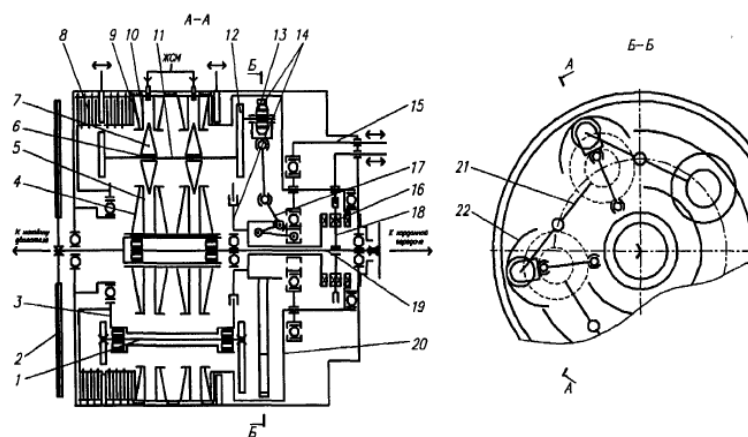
Схема автоматической бесступенчатой коробки передач автомобиля на основе нового планетарного дискового адаптивного вариатора: 1 — ось поворотных рычагов; 2 - соединительная муфта; 3 — водило; 4 — тарельчатая пружина; 5 — внутренний центральный фрикционный диск; 6 - подшипники сателлитов; 7 - сателлит; 8 — фрикционы; 9 — плоская дисковая пружина; 10 — внешний центральный фрикционный диск; 11 — ось сателлитов; 12 — противовес; 13 — ролик; 14 — кулачковый регулятор; 15 — шток; 16 — зубчатая полумуфта; 17 -рычажный механизм; 18 - каретка; 19 — выходной вал; 20 — эпицикл; 21 — поворотный рычаг; 22 — рабочая поверхность кулачкового регулятора; ЖСМ— жидкий смазочный материал [1]
